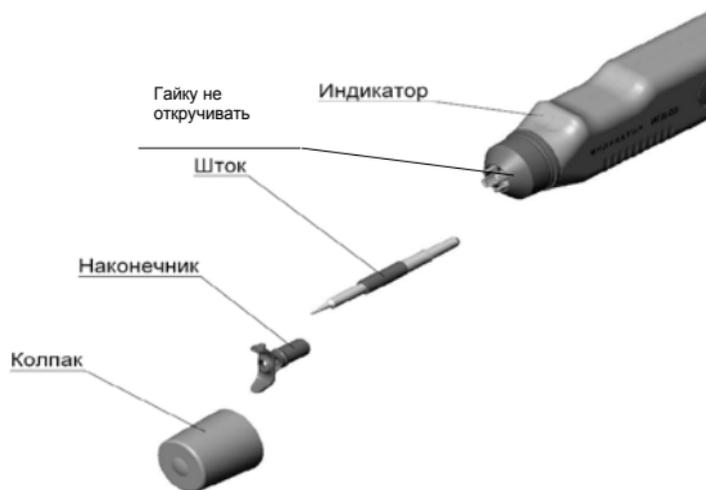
Подготовка индикатора к очистке штокового механизма
